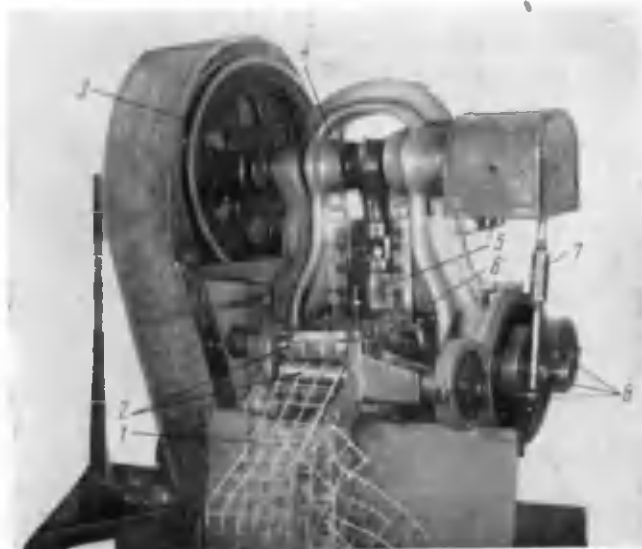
Эксцентриковый пресс для вырубki картонных деталей:
